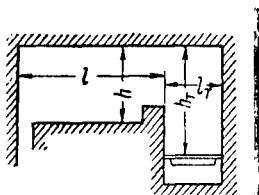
Схема печи, работающей на твердом топливе (с площадью пода ниже 3 м^2)
